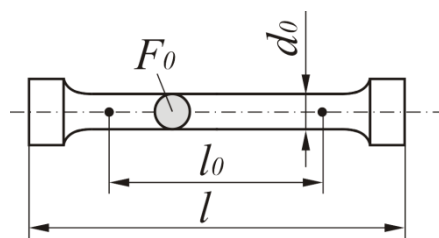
Цилиндрический образец для испытания на растяжение
